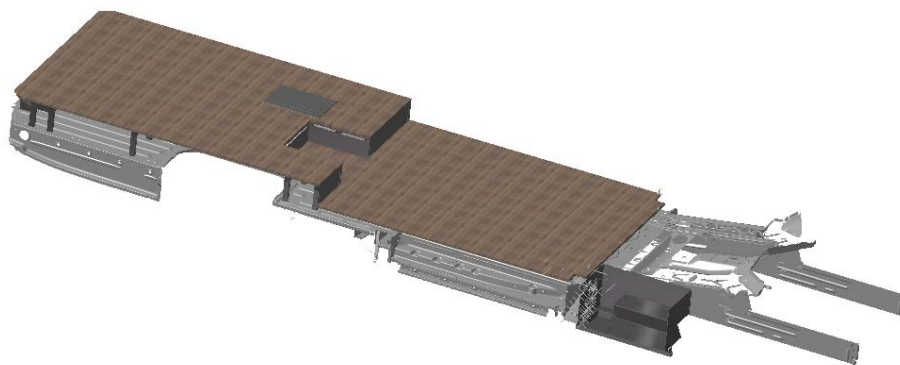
Colocación estribo puerta de servicio sobre vehículo.
